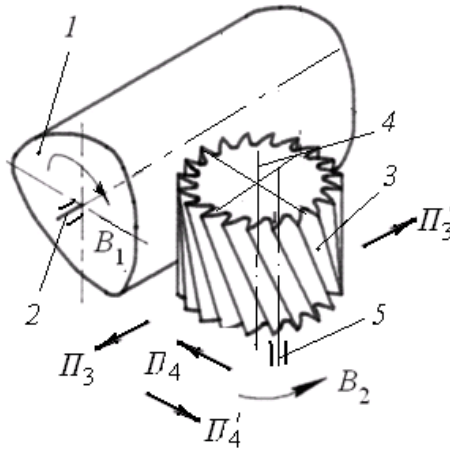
Кинематическая схема обработки некруглого вала эксцентрично установленной цилиндрической фрезой
